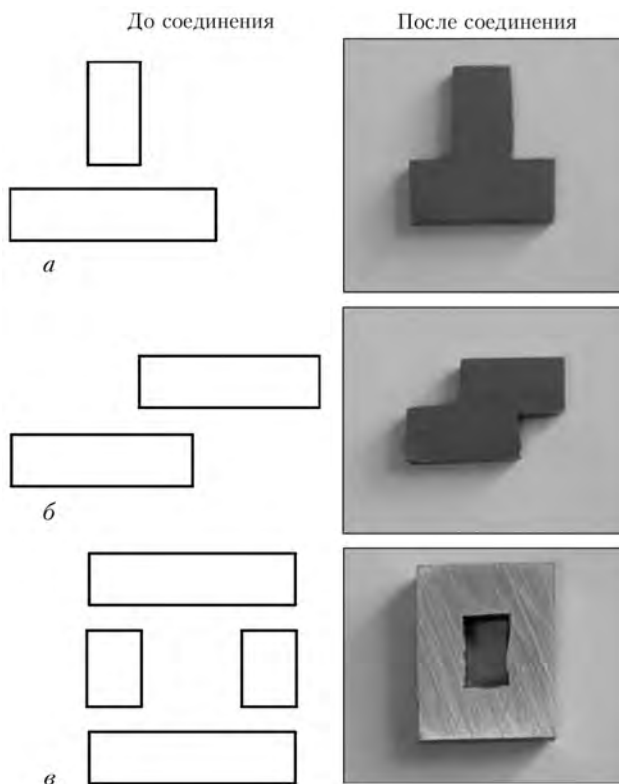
Общий вид сварных сборок Т-образной формы (а), внахлест (б) и коробчатого типа (в), полученных из сплава γ -TiAl через нанослойную фольгу Ti/Al
